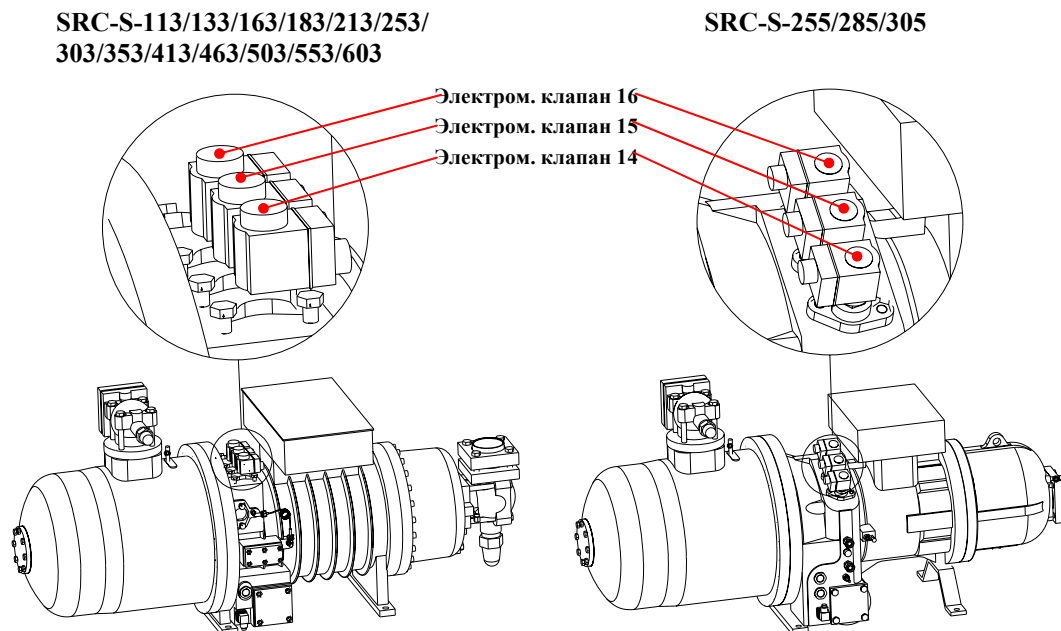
М: положение электромагнитного клапана в компрессоре;
